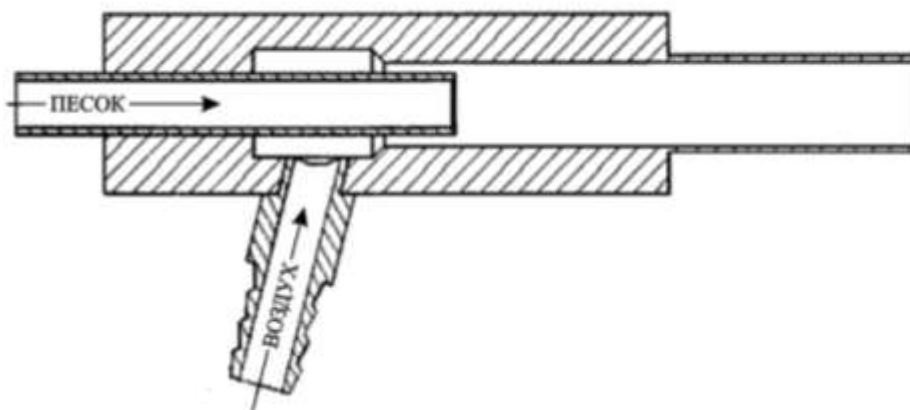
Схема пневматического пистолета для пескоструйной обработки
